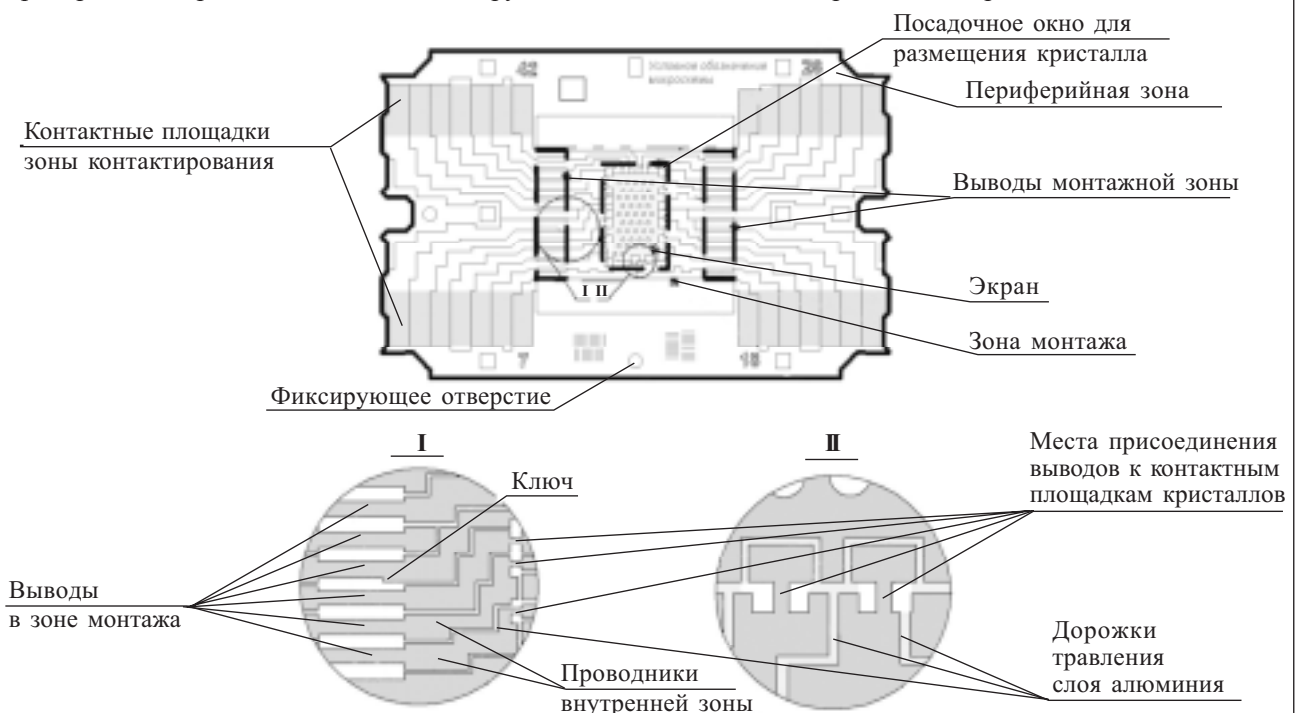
Гибкие полиимидный носитель для сборки микросхем (вид со стороны алюминия)
